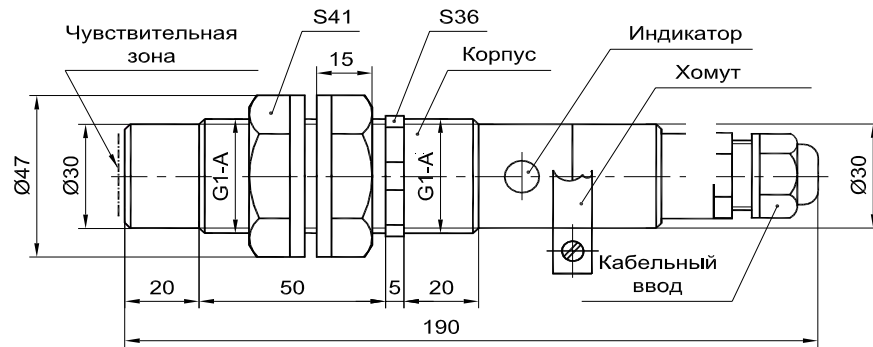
Внешний вид и габаритные размеры датчика
